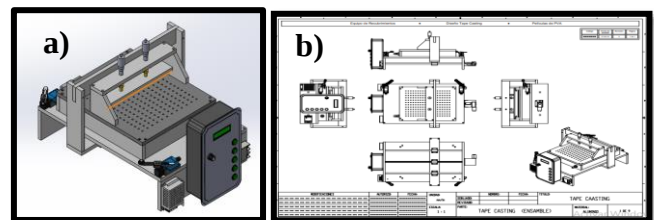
a) Ensamblaje de piezas para máquina Tape Casting, b) planos de máquina Tape Casting.
